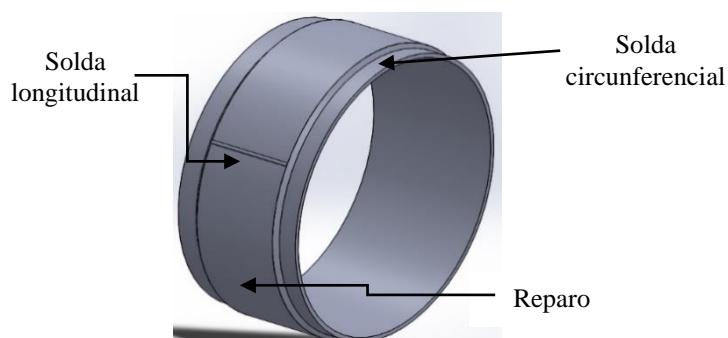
Modelagem completa do conjunto vaso de pressão-reparo-solda.
